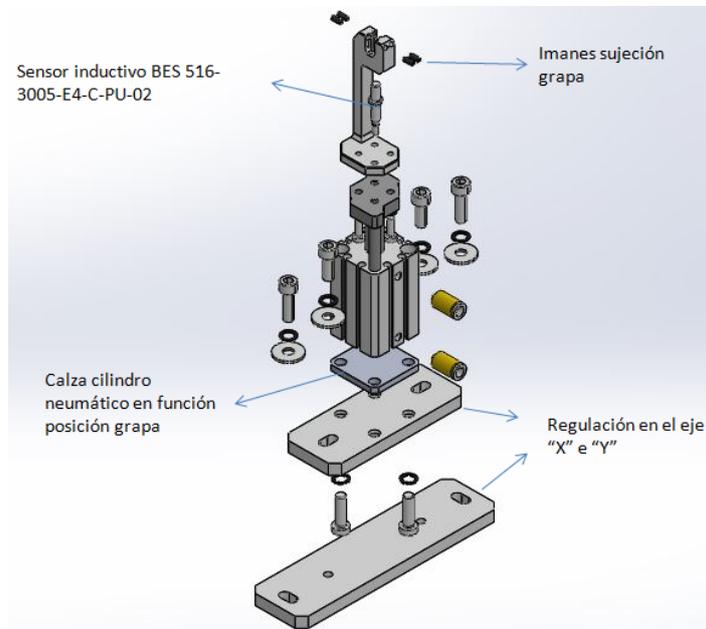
Porta grapas ensamblaje final (Vista Explosionada)
